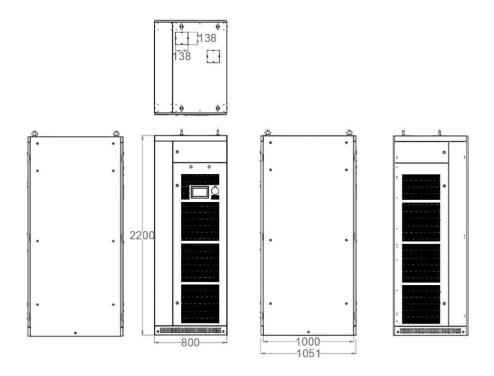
Внешние размеры стандартного шкафа 800*1000*2200
